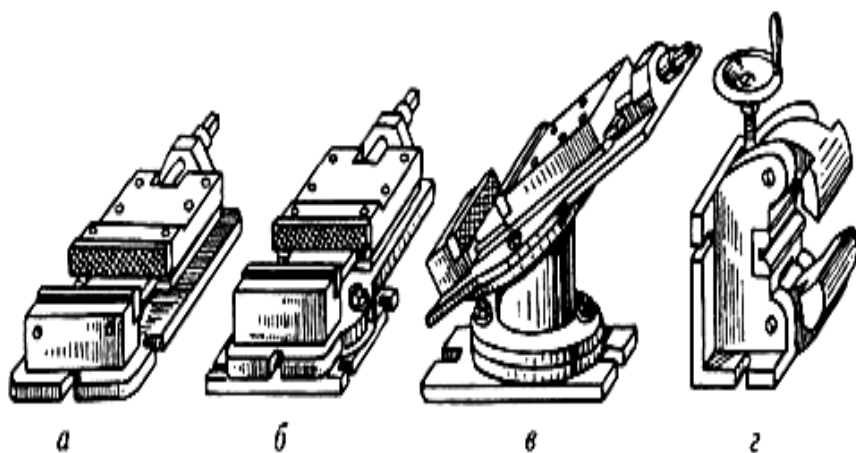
Машинные тиски: *а* – неповоротные; *б* – поворотные; *в* – универсальные; *г* – специальные
